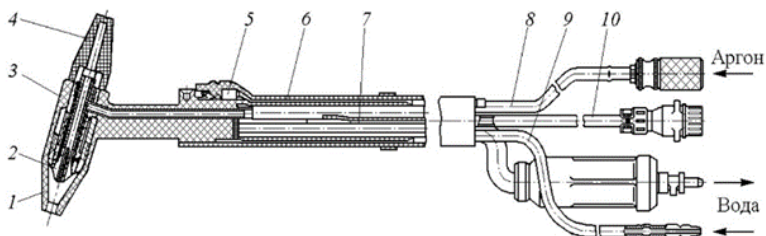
Горелки для сварки неплавящимся электродом
